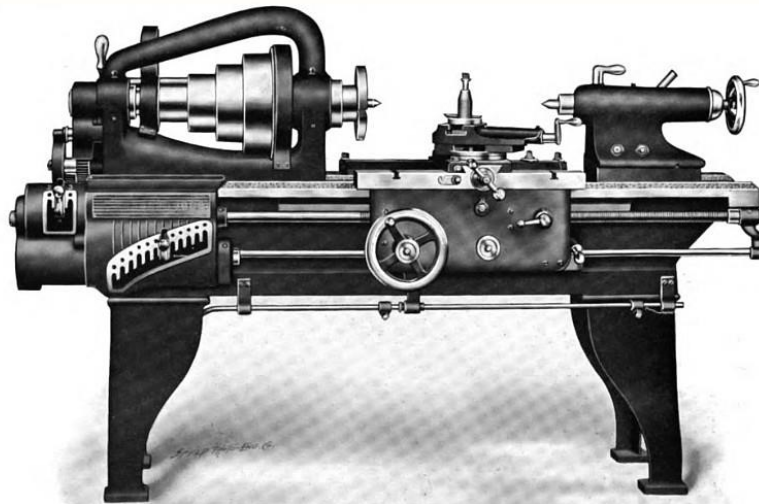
Torno de la empresa HENDEY MACHINE CO (1911) con la caja Norton incorporada. Fuente: Hendey Machine Co. <http://vintagemachinery.org/>
